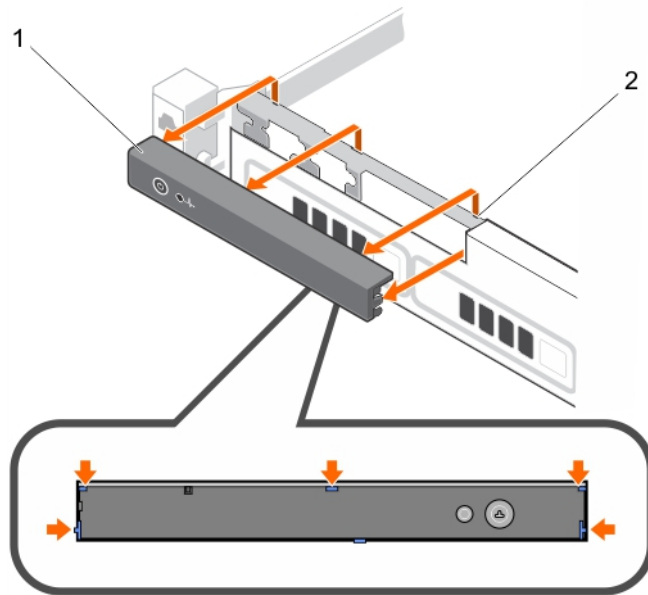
Entfernen des Bedienfelds – Gehäuse für vier 3,5 Zoll-Festplatten
